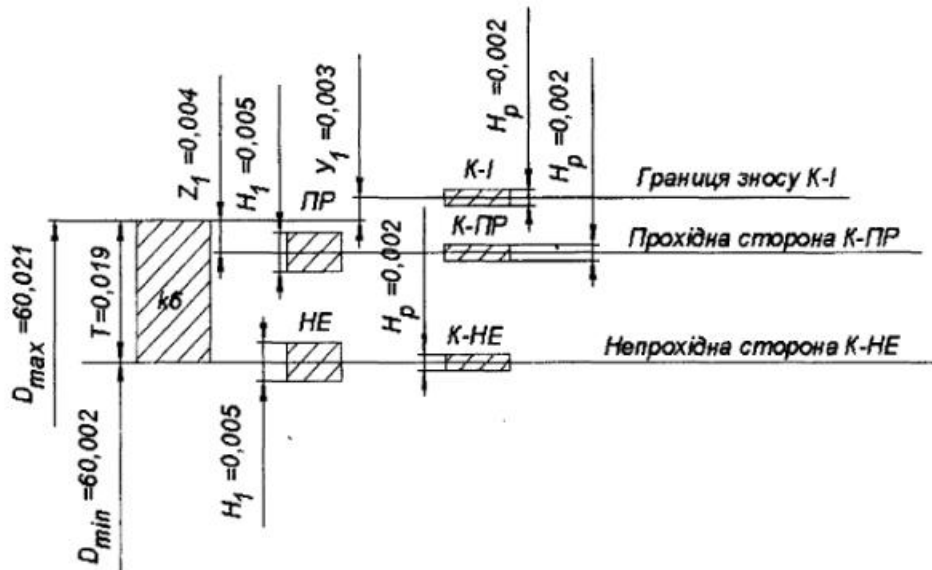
Схема розміщення полів допусків калібру.
